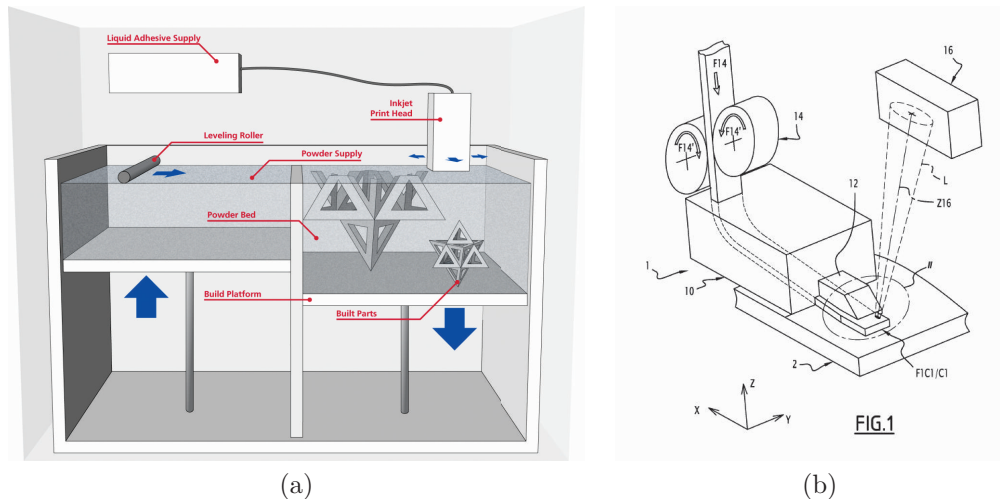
a) Procédé de binder jetting [7]; b) Procédé d’additive micro welding décrit par Teulet [8]
